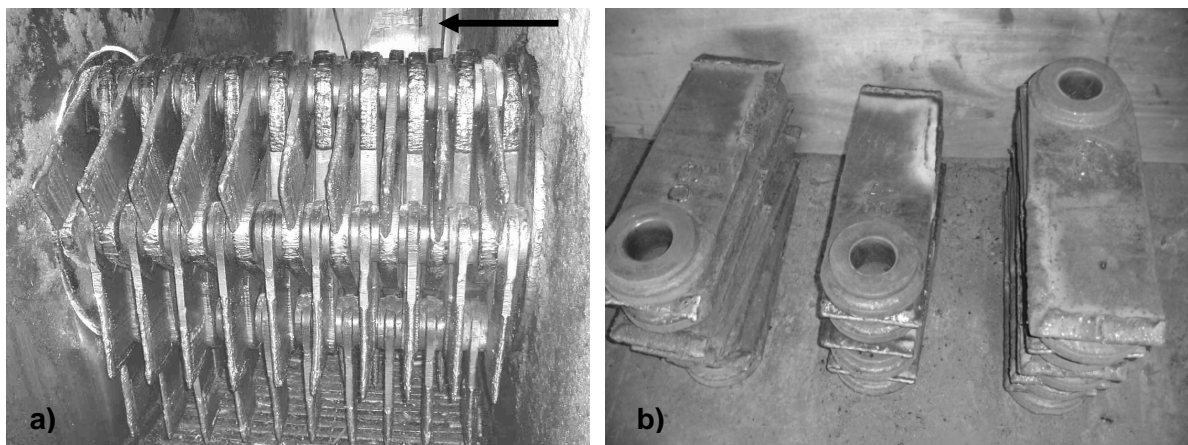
Vista interna do picador (a) e conjunto de facas picadoras (b). (Lima & Ferraresi, 2006).
